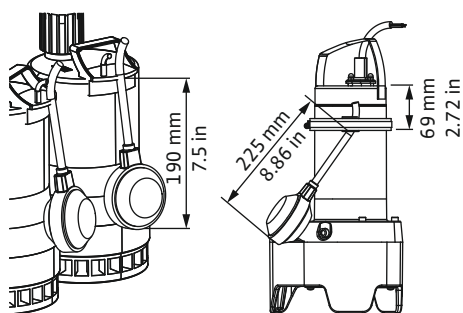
Крепление и настройка поплавкового выключателя, без прибора управления
